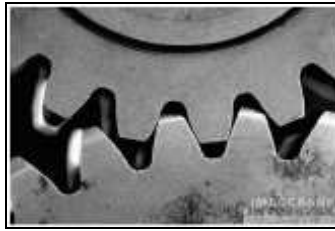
Exemplo de uma engrenagem de dentadura recta.
